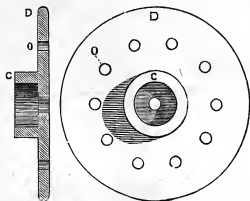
Disques fixateurs de M. le Dr COURTIN.
